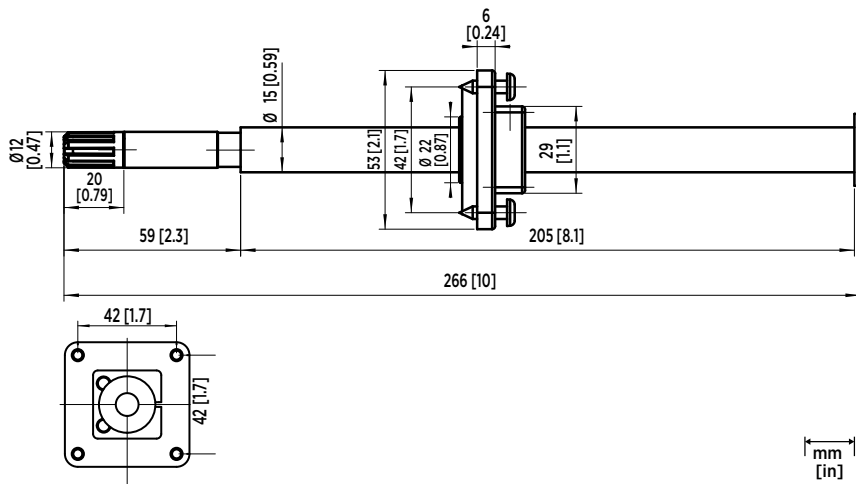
Dimensions de la sonde HMP110 avec kit d'installation pour conduit
